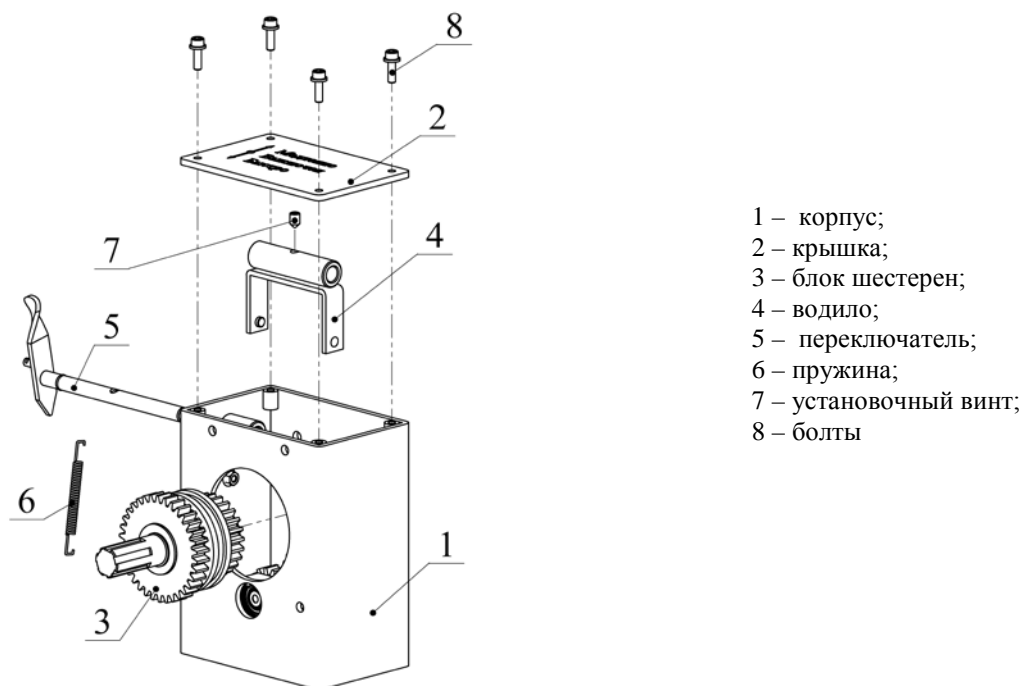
Схема подготовки ходоуменьшителя к монтажу
